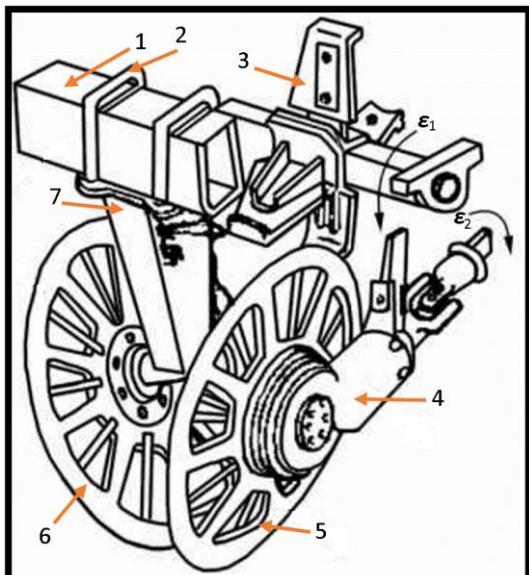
Схемное изображение копачей самоходной корнеуборочной машины КС-6Б: 1 – поперечный рамы секции ;2 – хомут крепления; 3 – стойка битера; 4 – редуктор конический привода диска копача; 5 – диск копача принудительно вращающийся; 6 – диск копача; 7 – стойка копача; $\varepsilon_1$  – направление вращения дисков;  $\varepsilon_2$  – направление вращения вала редуктора.
